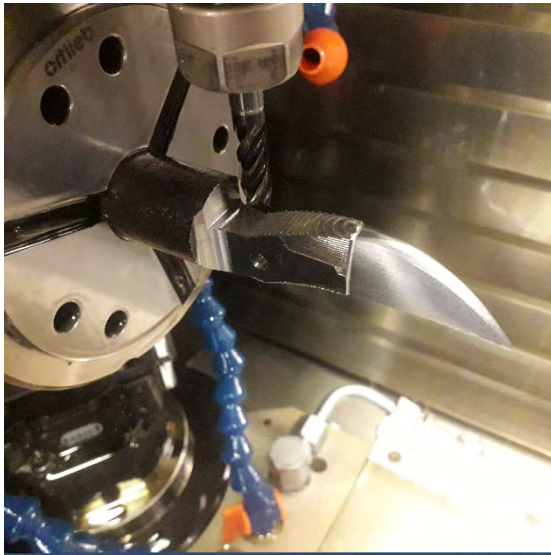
Черновое фрезерование оставшейся части длины детали
